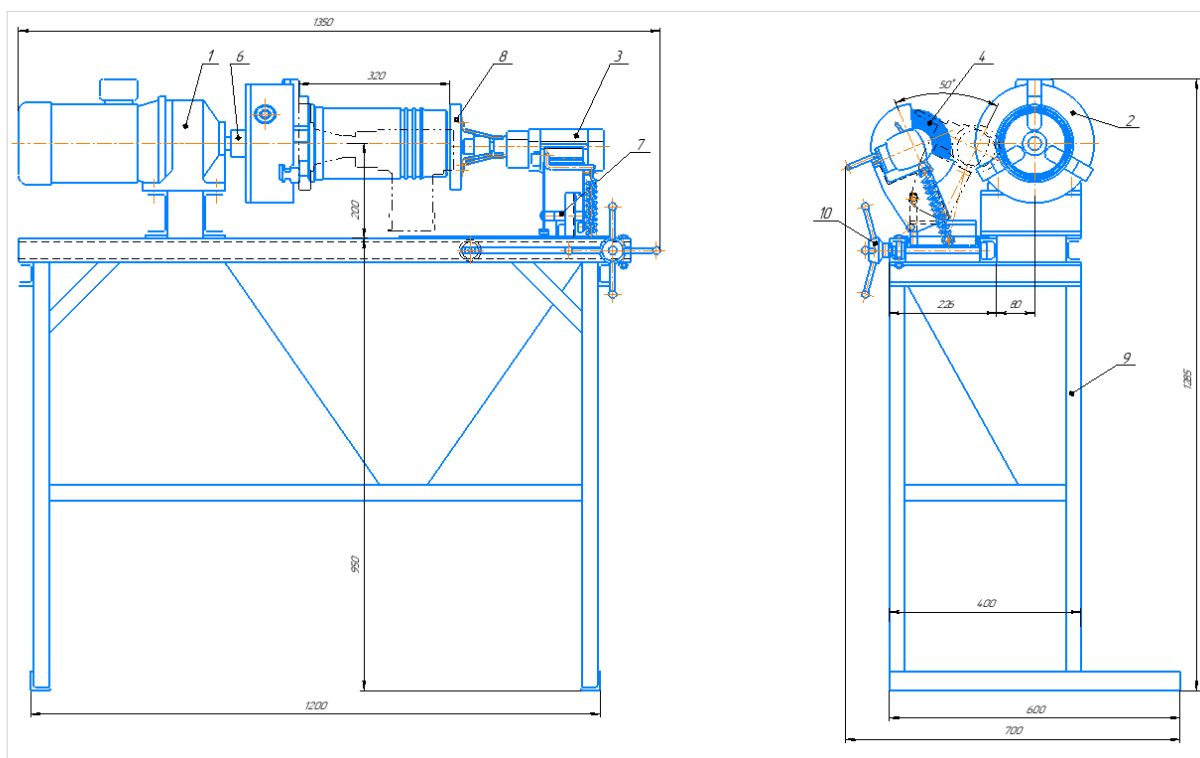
Загальний вид установки для крацювання циліндричних деталей
